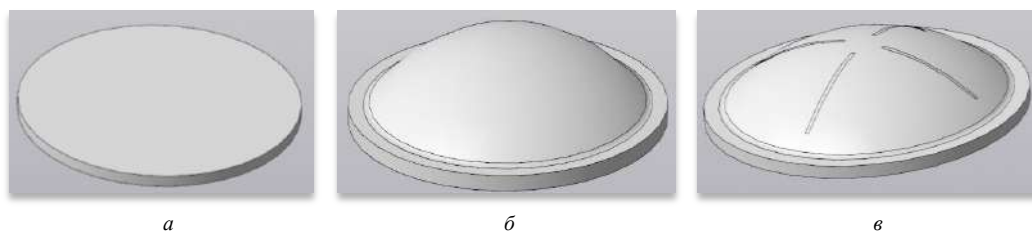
Исходная заготовка-рondоль (а); полуфабрикат после формообразования рабочей части (б); мембрана с нанесенными насечками (в)
